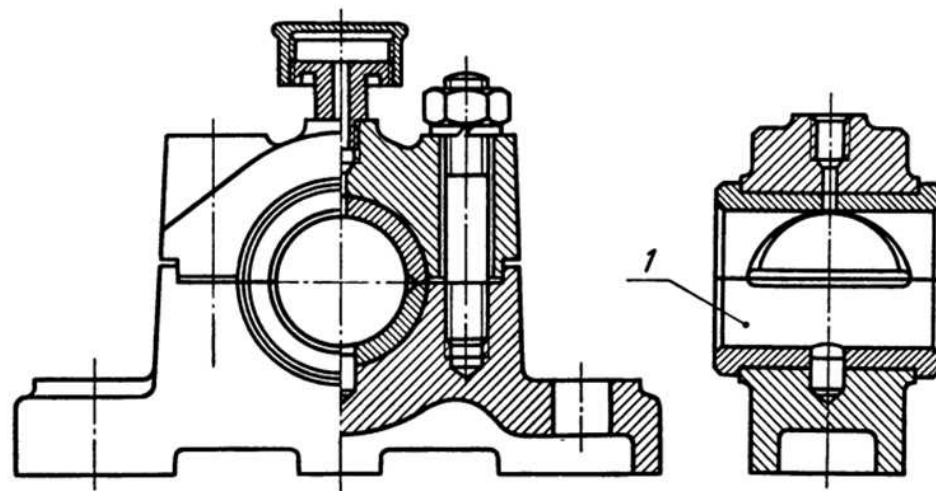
Подшипник с разъемным корпусом и вкладышем
